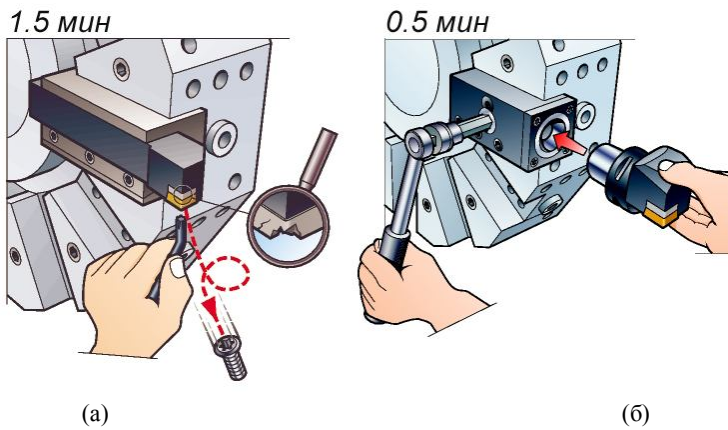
Замена инструмента на револьверной головке со стандартным креплением (а) и с механизмом с лепестковой цангой (б)
